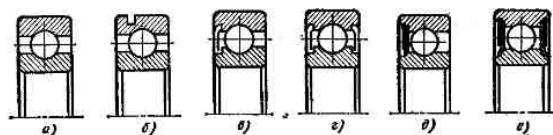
Шарикоподшипники радиальные однорядные типов: а — 0000; б — 5600; в — 6000; г — 8000; д — 16000; е — 18000
